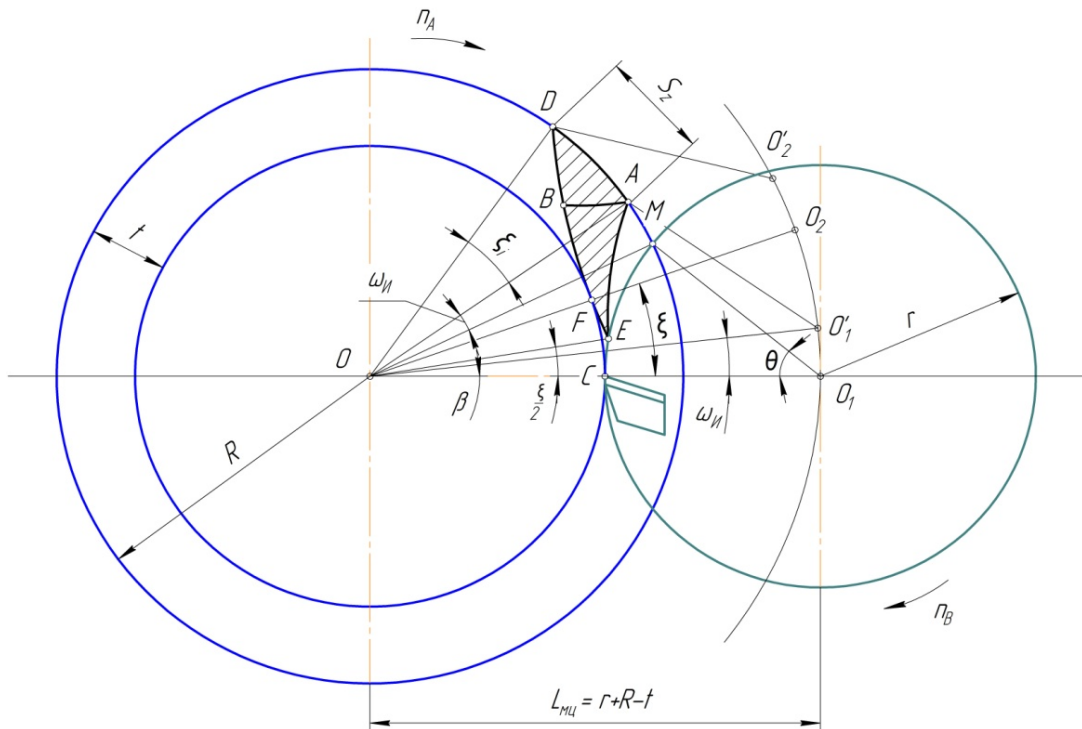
Схема фрезерования резьбы дисковой фрезой на всю глубину припуска
